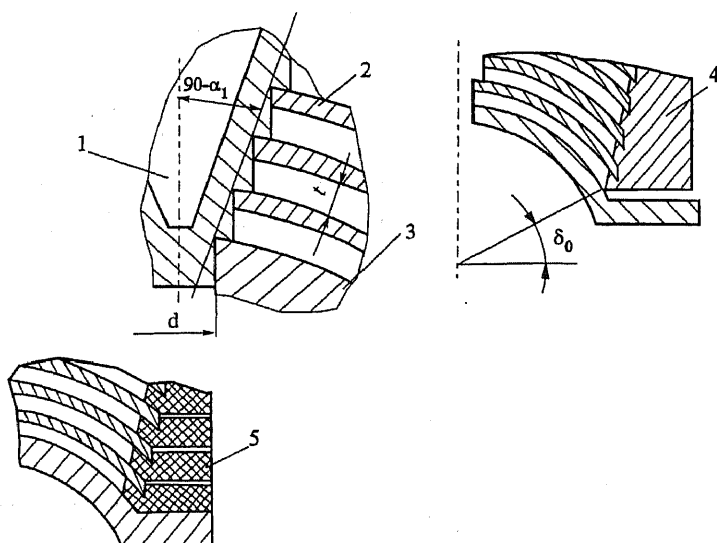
Элементы пресс-формы для изготовления сферического эластомерного подшипника:
